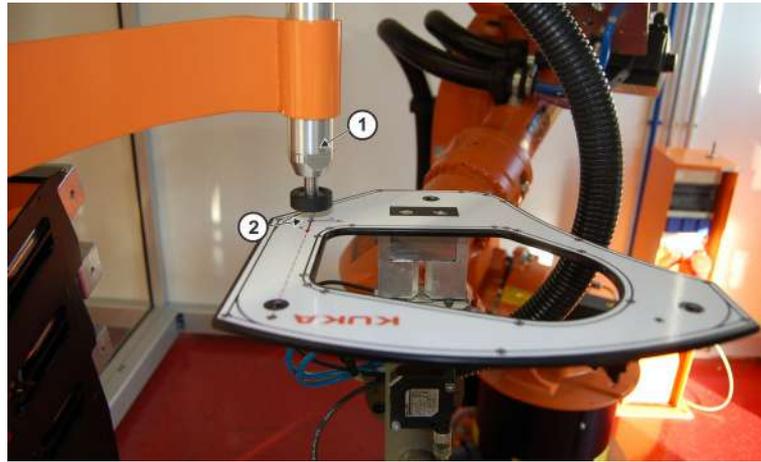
Componente 3D en la herramienta de engrapado externa
